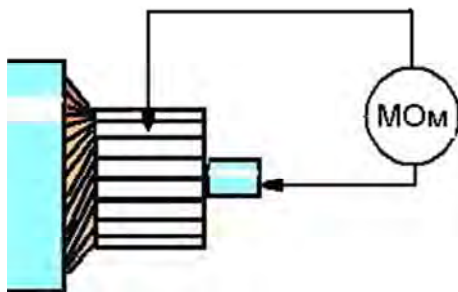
Проверка сопротивления между ламелями и корпусом
